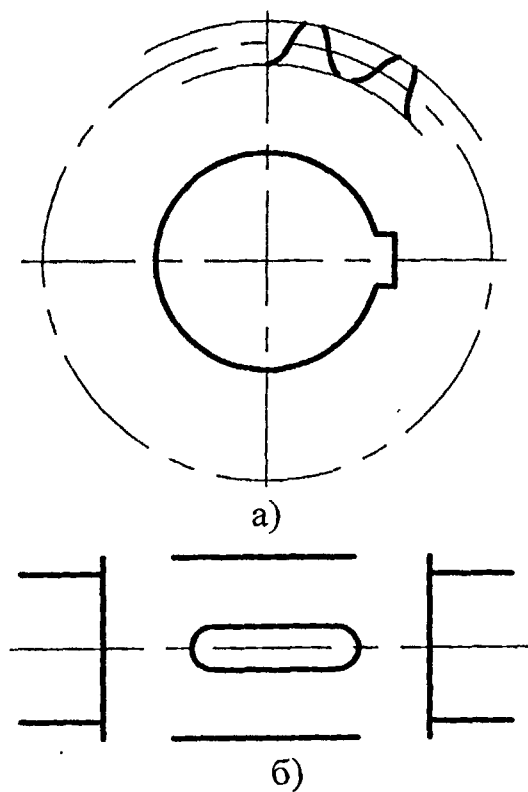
Представление деталей машин совокупностью исполнительных поверхностей: а) зубчатое колесо; б) вал
